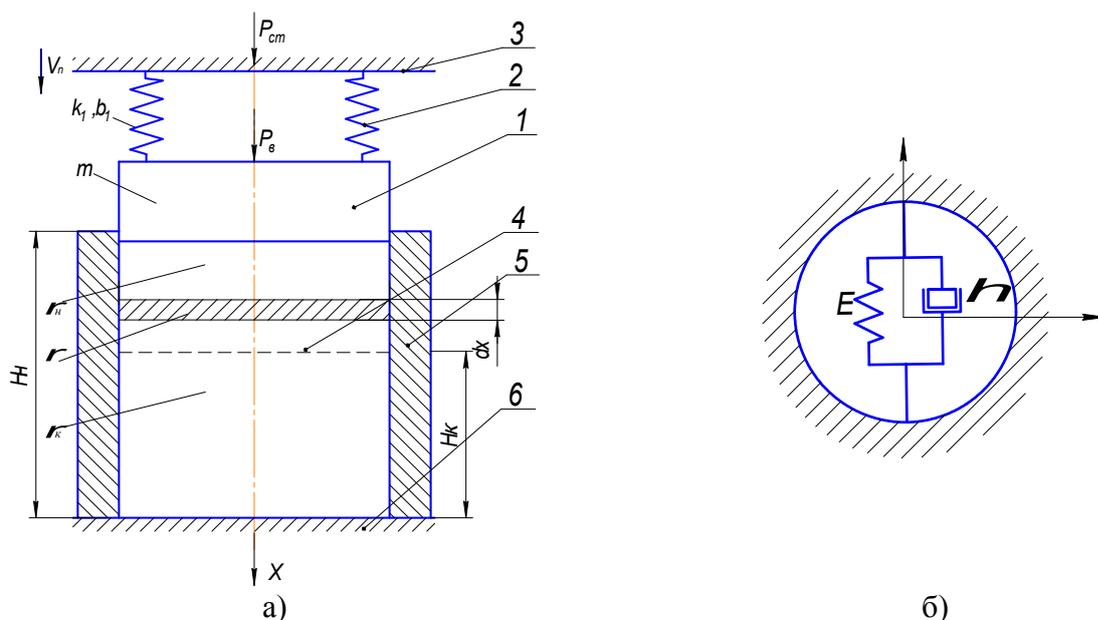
Схема процесса деформирования порошковой заготовки (1 – пуансон; 2 – пружина; 3 – нажимная плита; 4 – порошковая заготовка; 5 – пресс-форма; 6 – основание пресс-формы):
